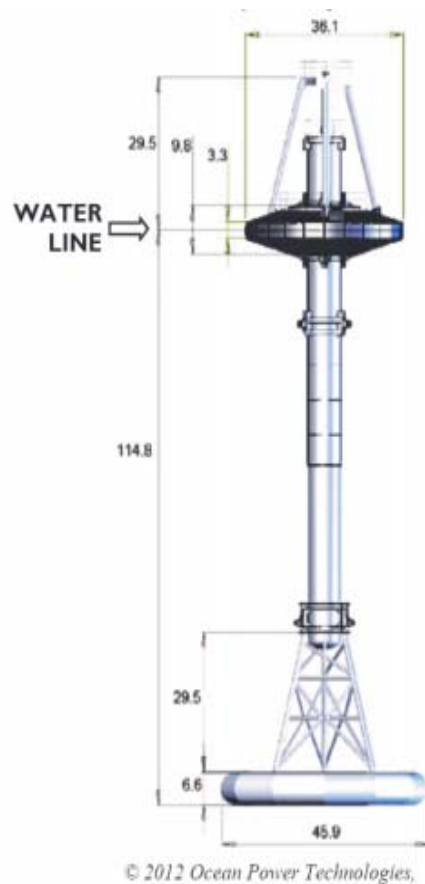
Dimensiones del dispositivo Power Buoy en pies
